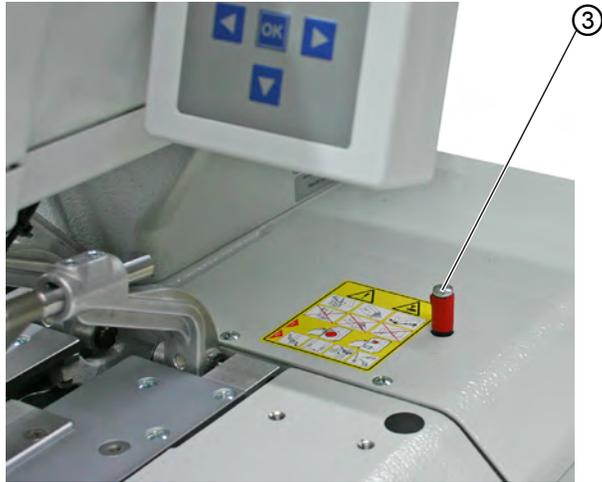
Remover os dispositivos de fixação utilizados no transporte das placas de fixação
